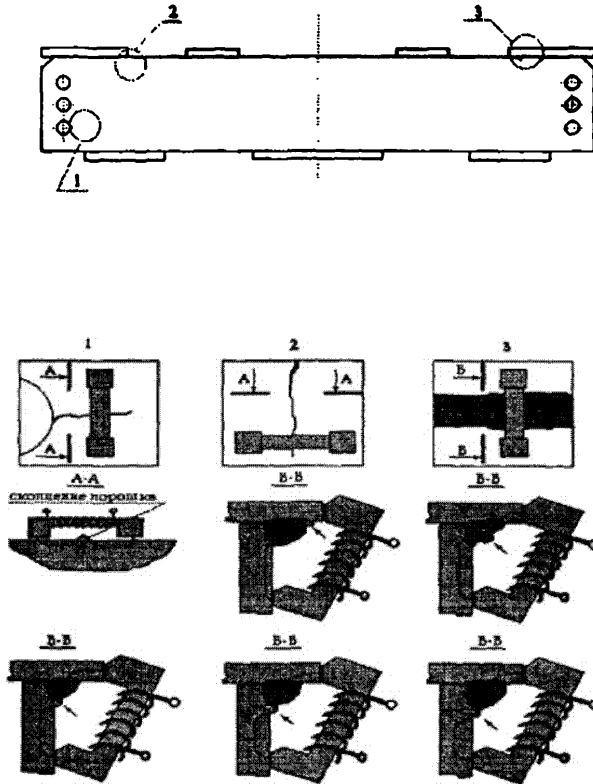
Магнитопорошковый контроль верхней балки кабины ( пример ).
